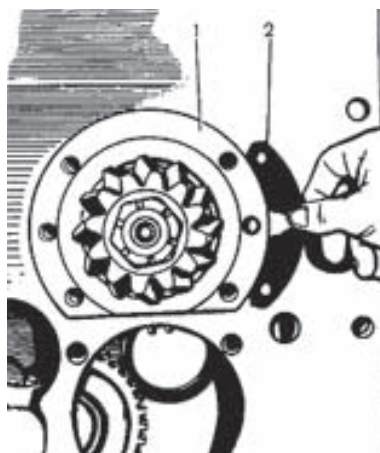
Регулировка осевого зазора в подшипниках вторичного вала: 1 — стакан подшипника вторичного вала; 2 — регулировочные прокладки
